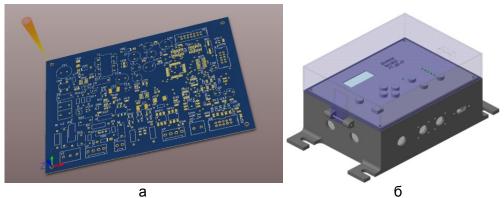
D-модель конструктива основной ПП (а); разработанный корпус ЭБУ (б)
